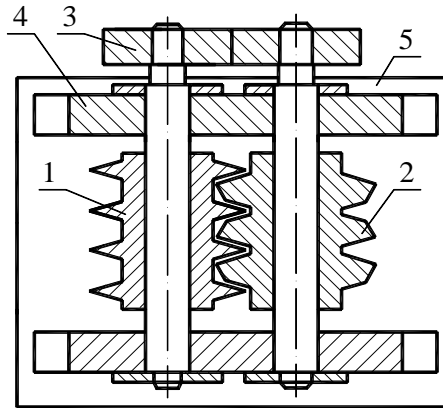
Валковий пристрій для подрібнення полімерної плівки:
